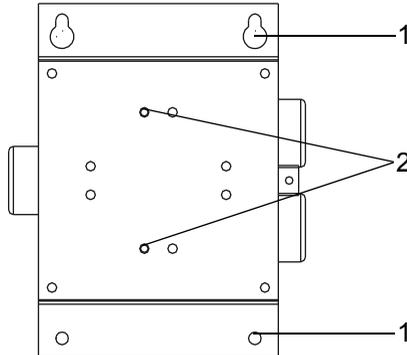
Placa de montaje para ULTIMA XE y XIR
